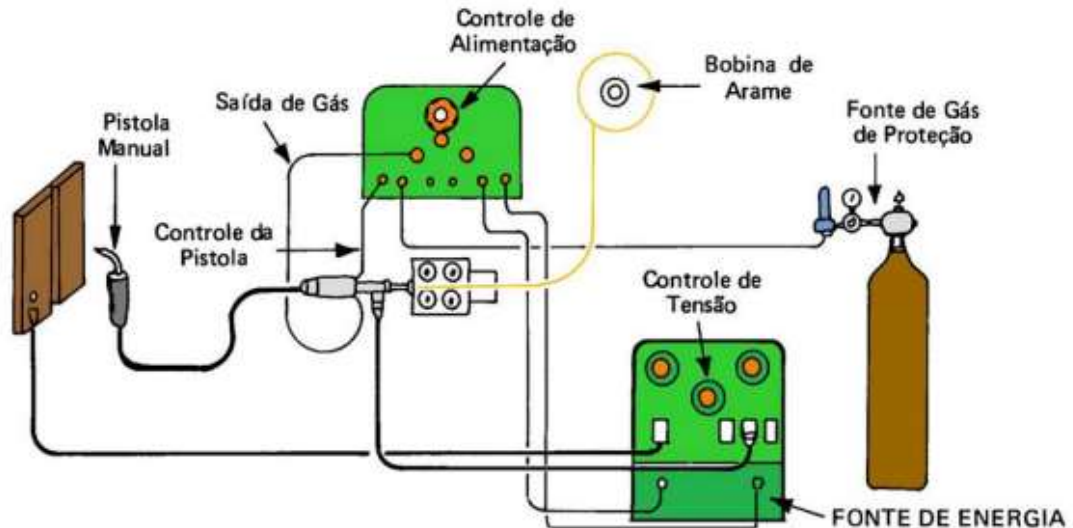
Esquema de montagem para soldagem MIG/MAG⁽³¹⁾.
